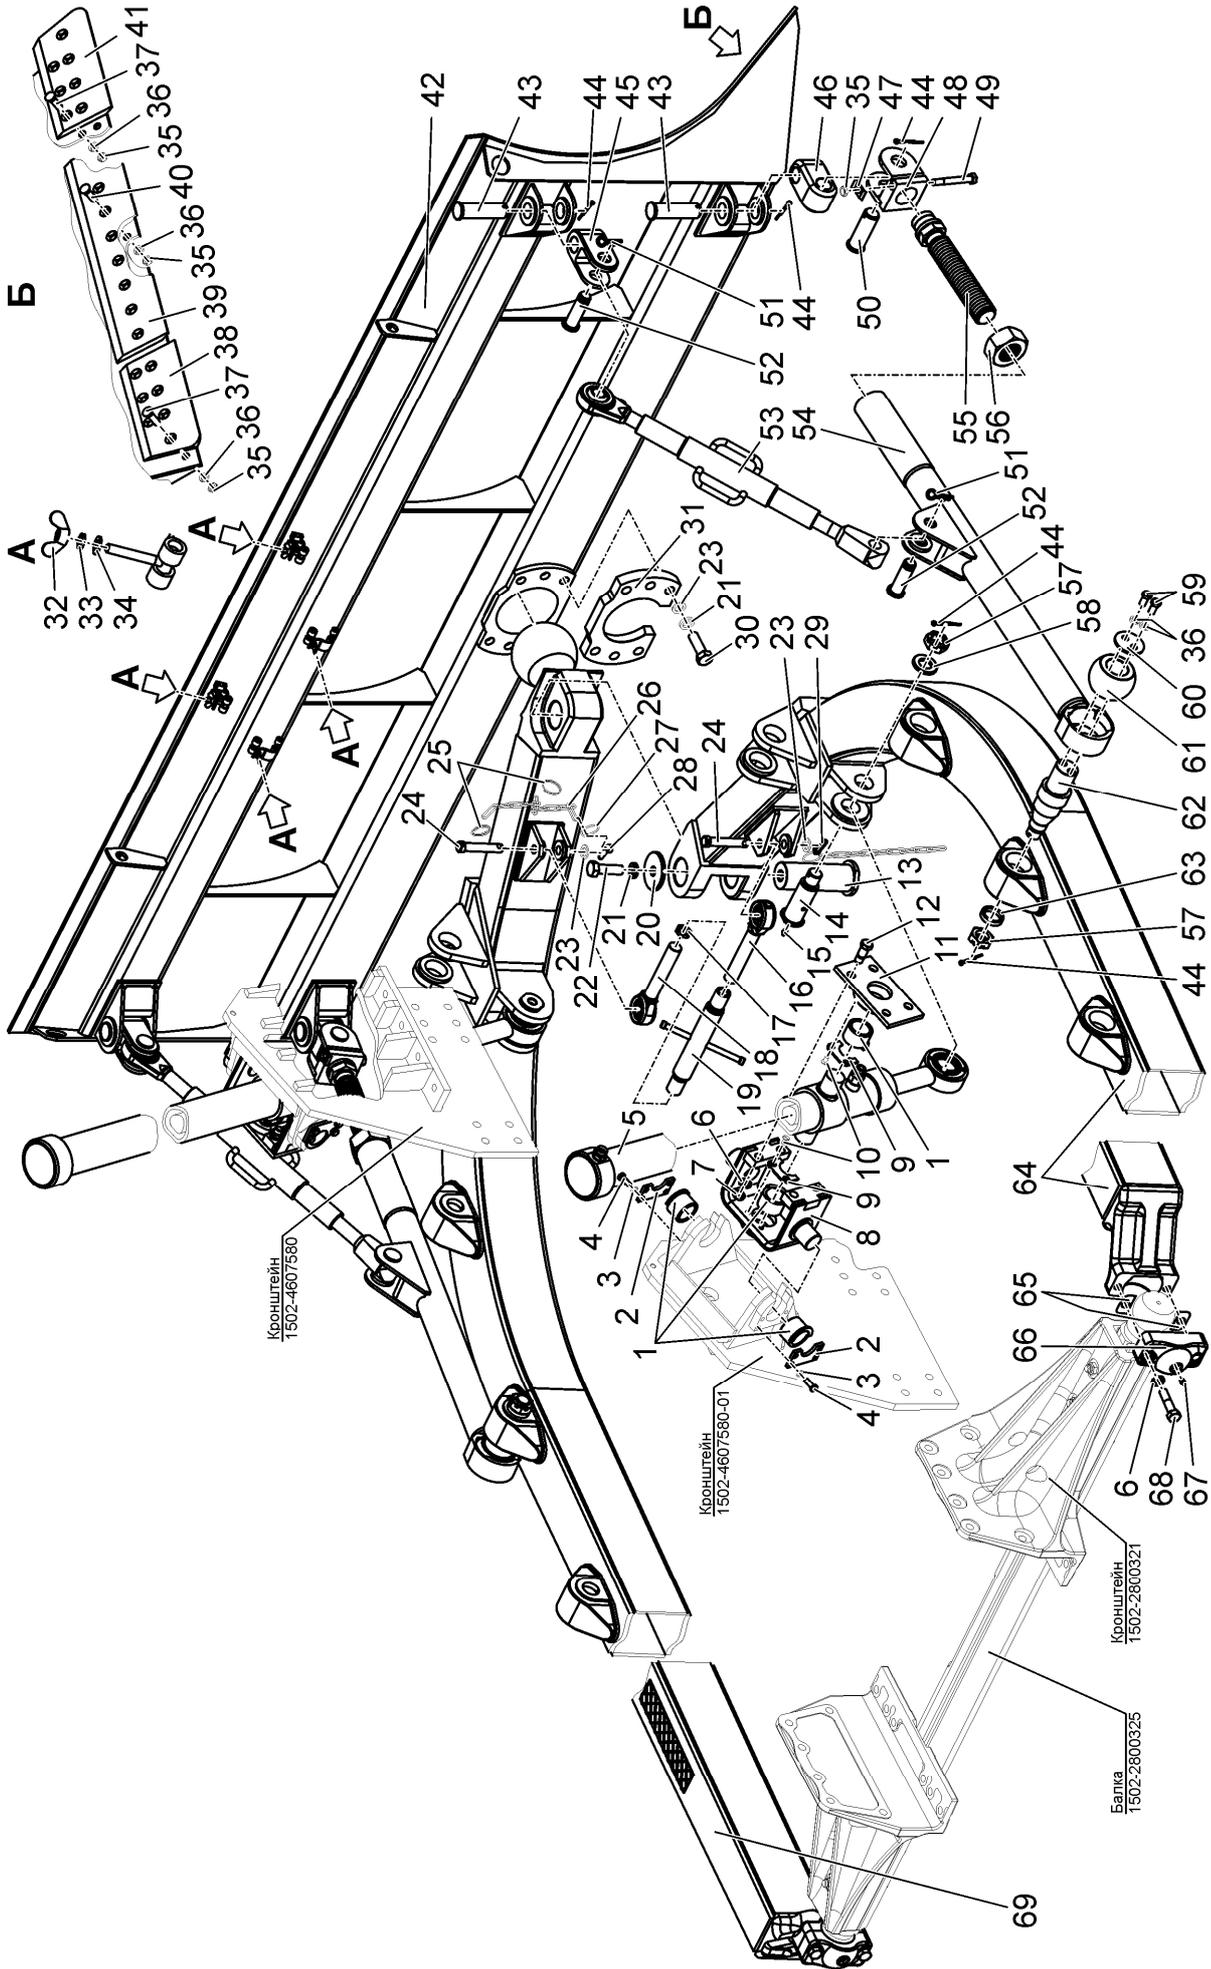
Установка отвала. Вилка. Тяга верхняя. Винт
